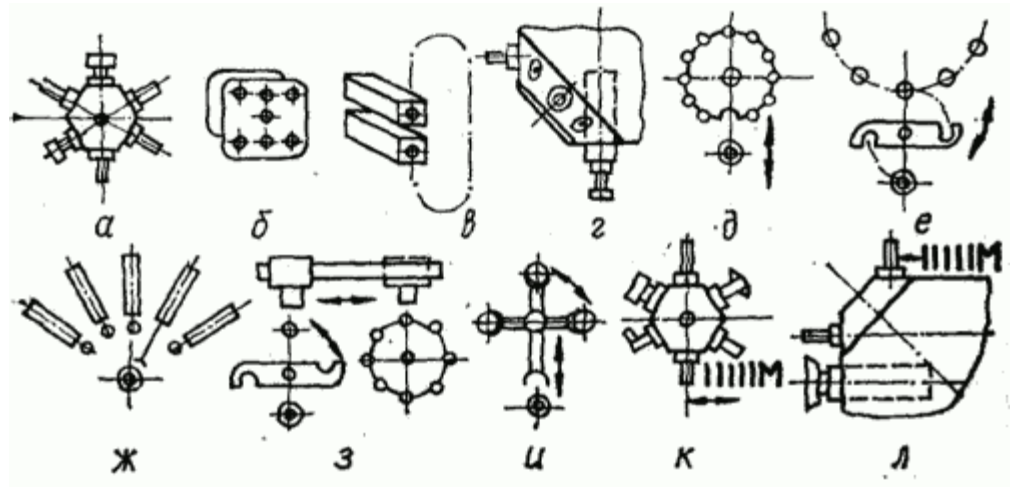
Конструктивний вигляд пристроїв АЗМ
